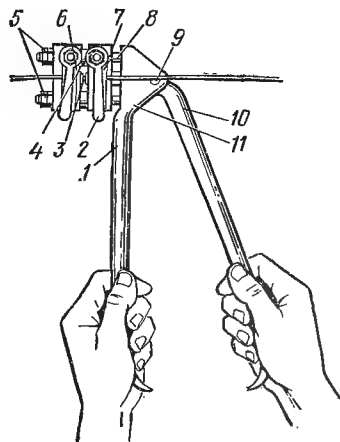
Ручные сварочные клещи КС-6:
